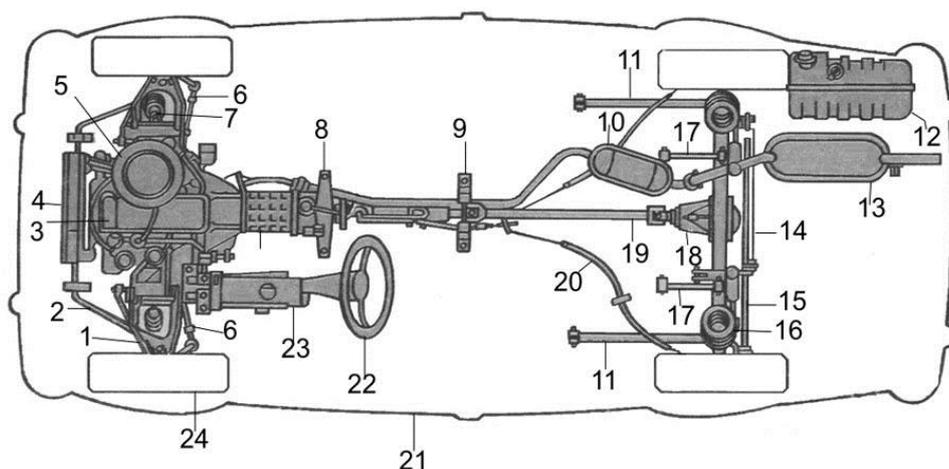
Общая компоновка узлов и агрегатов легкового автомобиля с приводом на задние колеса. 1 – рычаг передней подвески; 2 – стабилизатор поперечной устойчивости; 3 – двигатель; 4 – радиатор; 5 – корпус фильтра очистки воздуха; 6 – рулевые тяги; 7 – амортизатор передней подвески; 8 – опора силового агрегата; 9 – промежуточная опора карданного вала; 10 – резонатор системы выпуска отработавших газов; 11 – тяги задней подвески; 12 – топливный бак; 13 – глушитель системы
